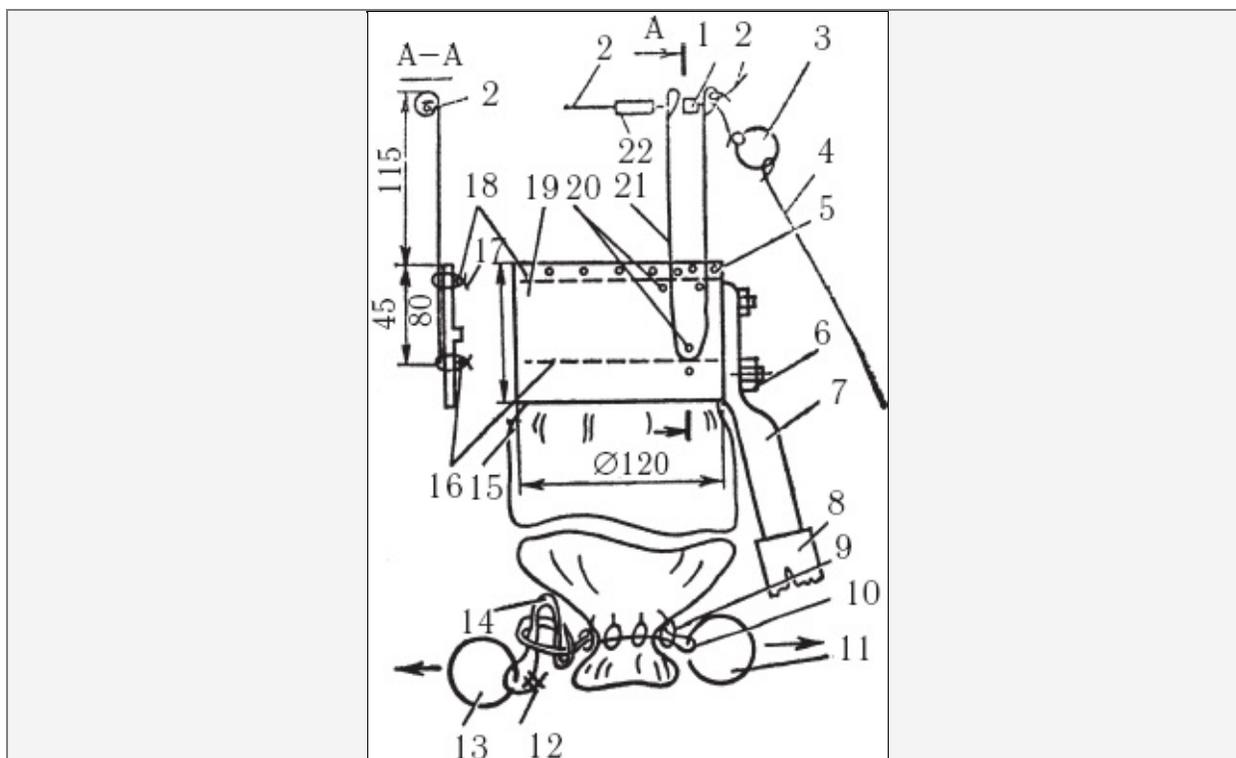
Плодосъемник с пружинящими пальцами: 1 – короткая трубка; 2 – стягивающая леска; 3 – ограничительное кольцо; 4 – шнур; 5 – отверстия для крепления мешка; 6 – болты крепления патрубка; 7 – патрубок для шеста; 8 – шест; 9, 11 и 13 – малые и большие кольца; 10 – стягивающий шнур; 12 – зажим; 14 – быстродействующий узел; 15 – плодосборный мешок; 16 и 18 – нижнее и верхнее проволочные кольца; 17 – скобы; 19 – корпус; 20 – отверстия для крепления пальцев; 21 – сдвоенные пружинящие пальцы; 22 – удлиненная трубка
